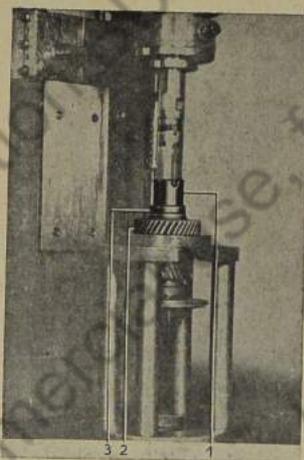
Laufbuchse zum Schrägrad für 2. Gang und Laufring für Zylinderrollenlager abpressen
